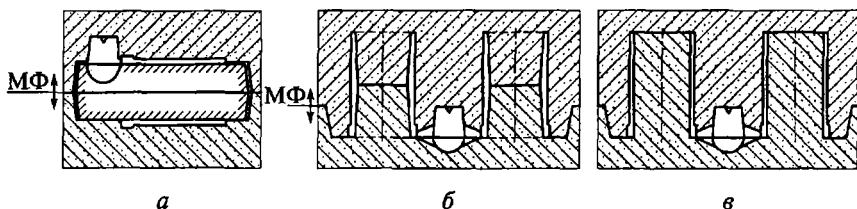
Разработка технологического процесса изготовления отливки гильзы цилиндров:
